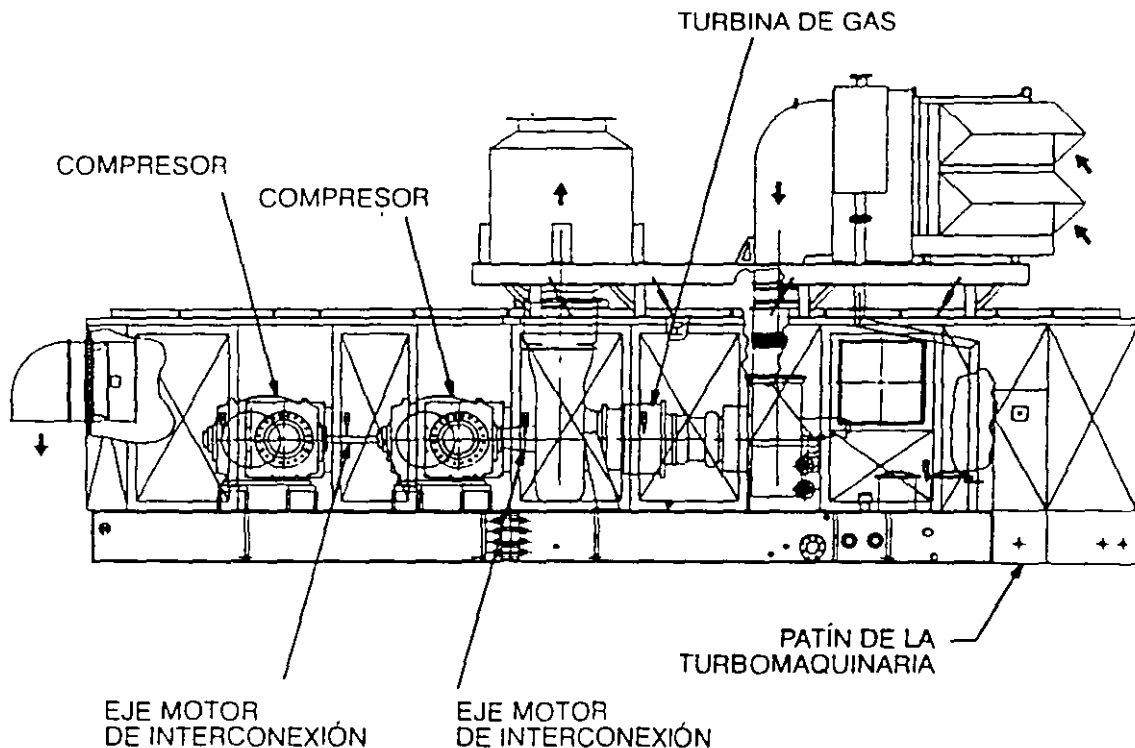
Conjunto compresor accionado por turbina de gas Centaur
